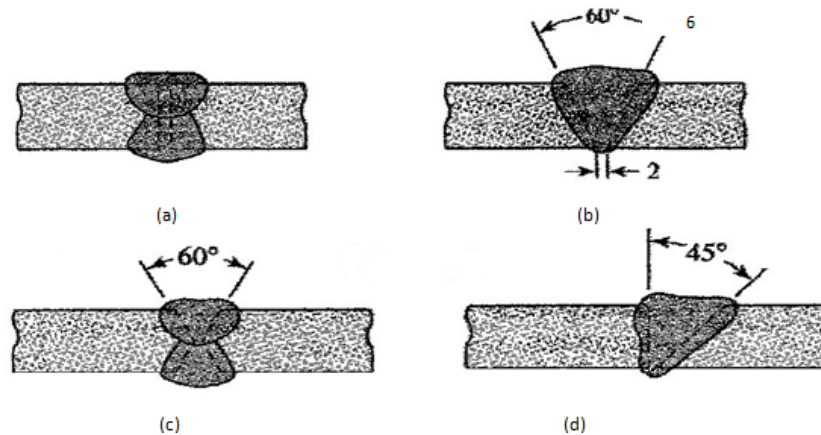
Soldaduras a Tope, sometidas a tracción o compresión: (a) tope con extremos rectos; (b) bisel a 60°; (c) doble bisel a 60°; (d) bisel simple a 45°.
